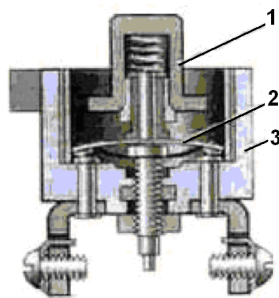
Устройство термобиметаллического предохранителя: 1 - кнопка возврата; 2 - биметаллическая пластина; 3 – корпус
